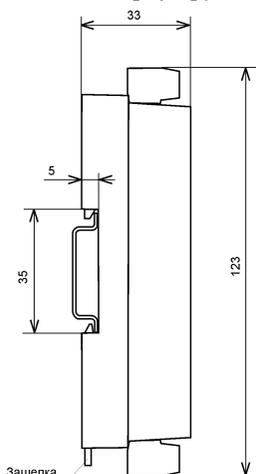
Габаритный чертеж модуля с креплением к DIN-рейке. Вид сбоку
